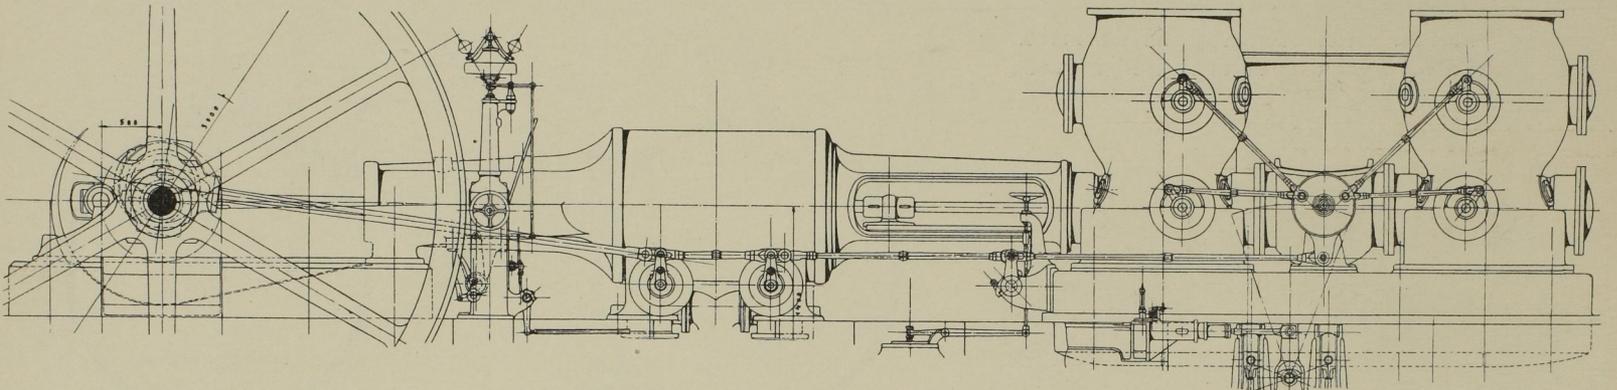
Seitenansicht der Pumpmaschine. Massst. 1:60.
